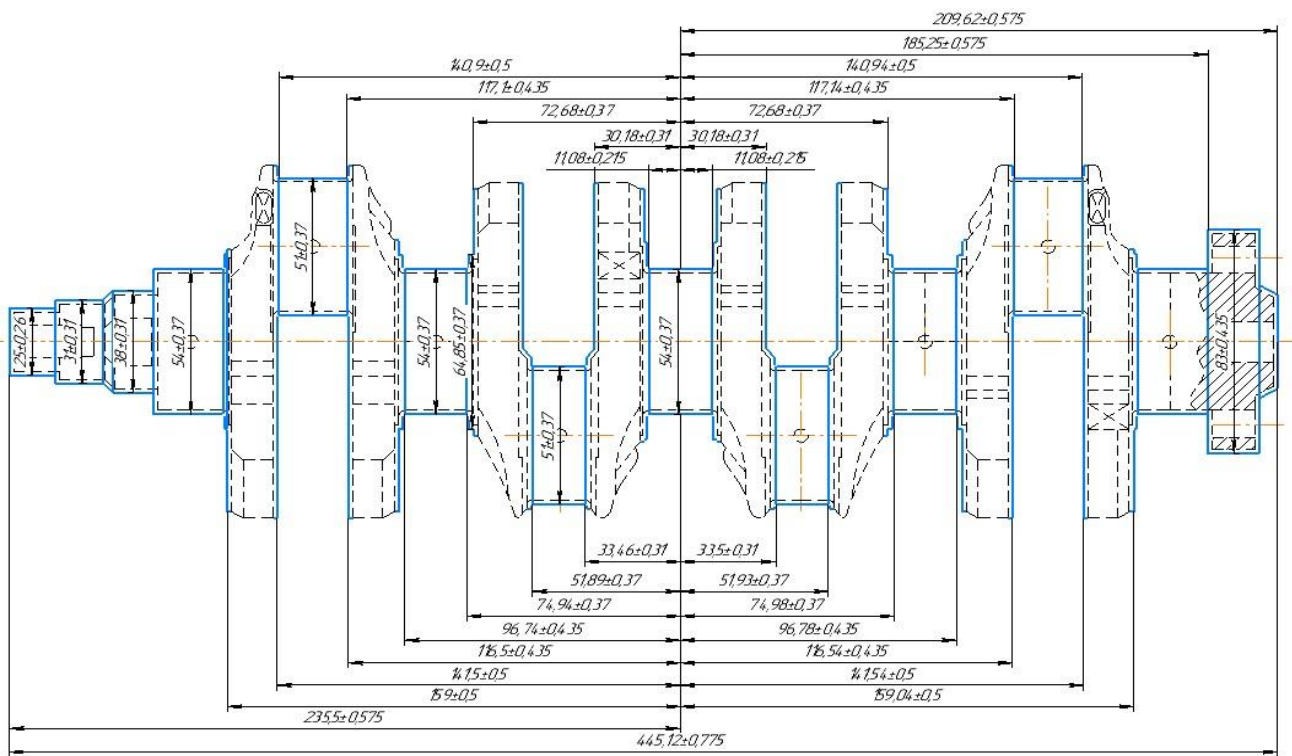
Чертеж заготовки коленчатого вала двигателя «ВАЗ – 11183»
